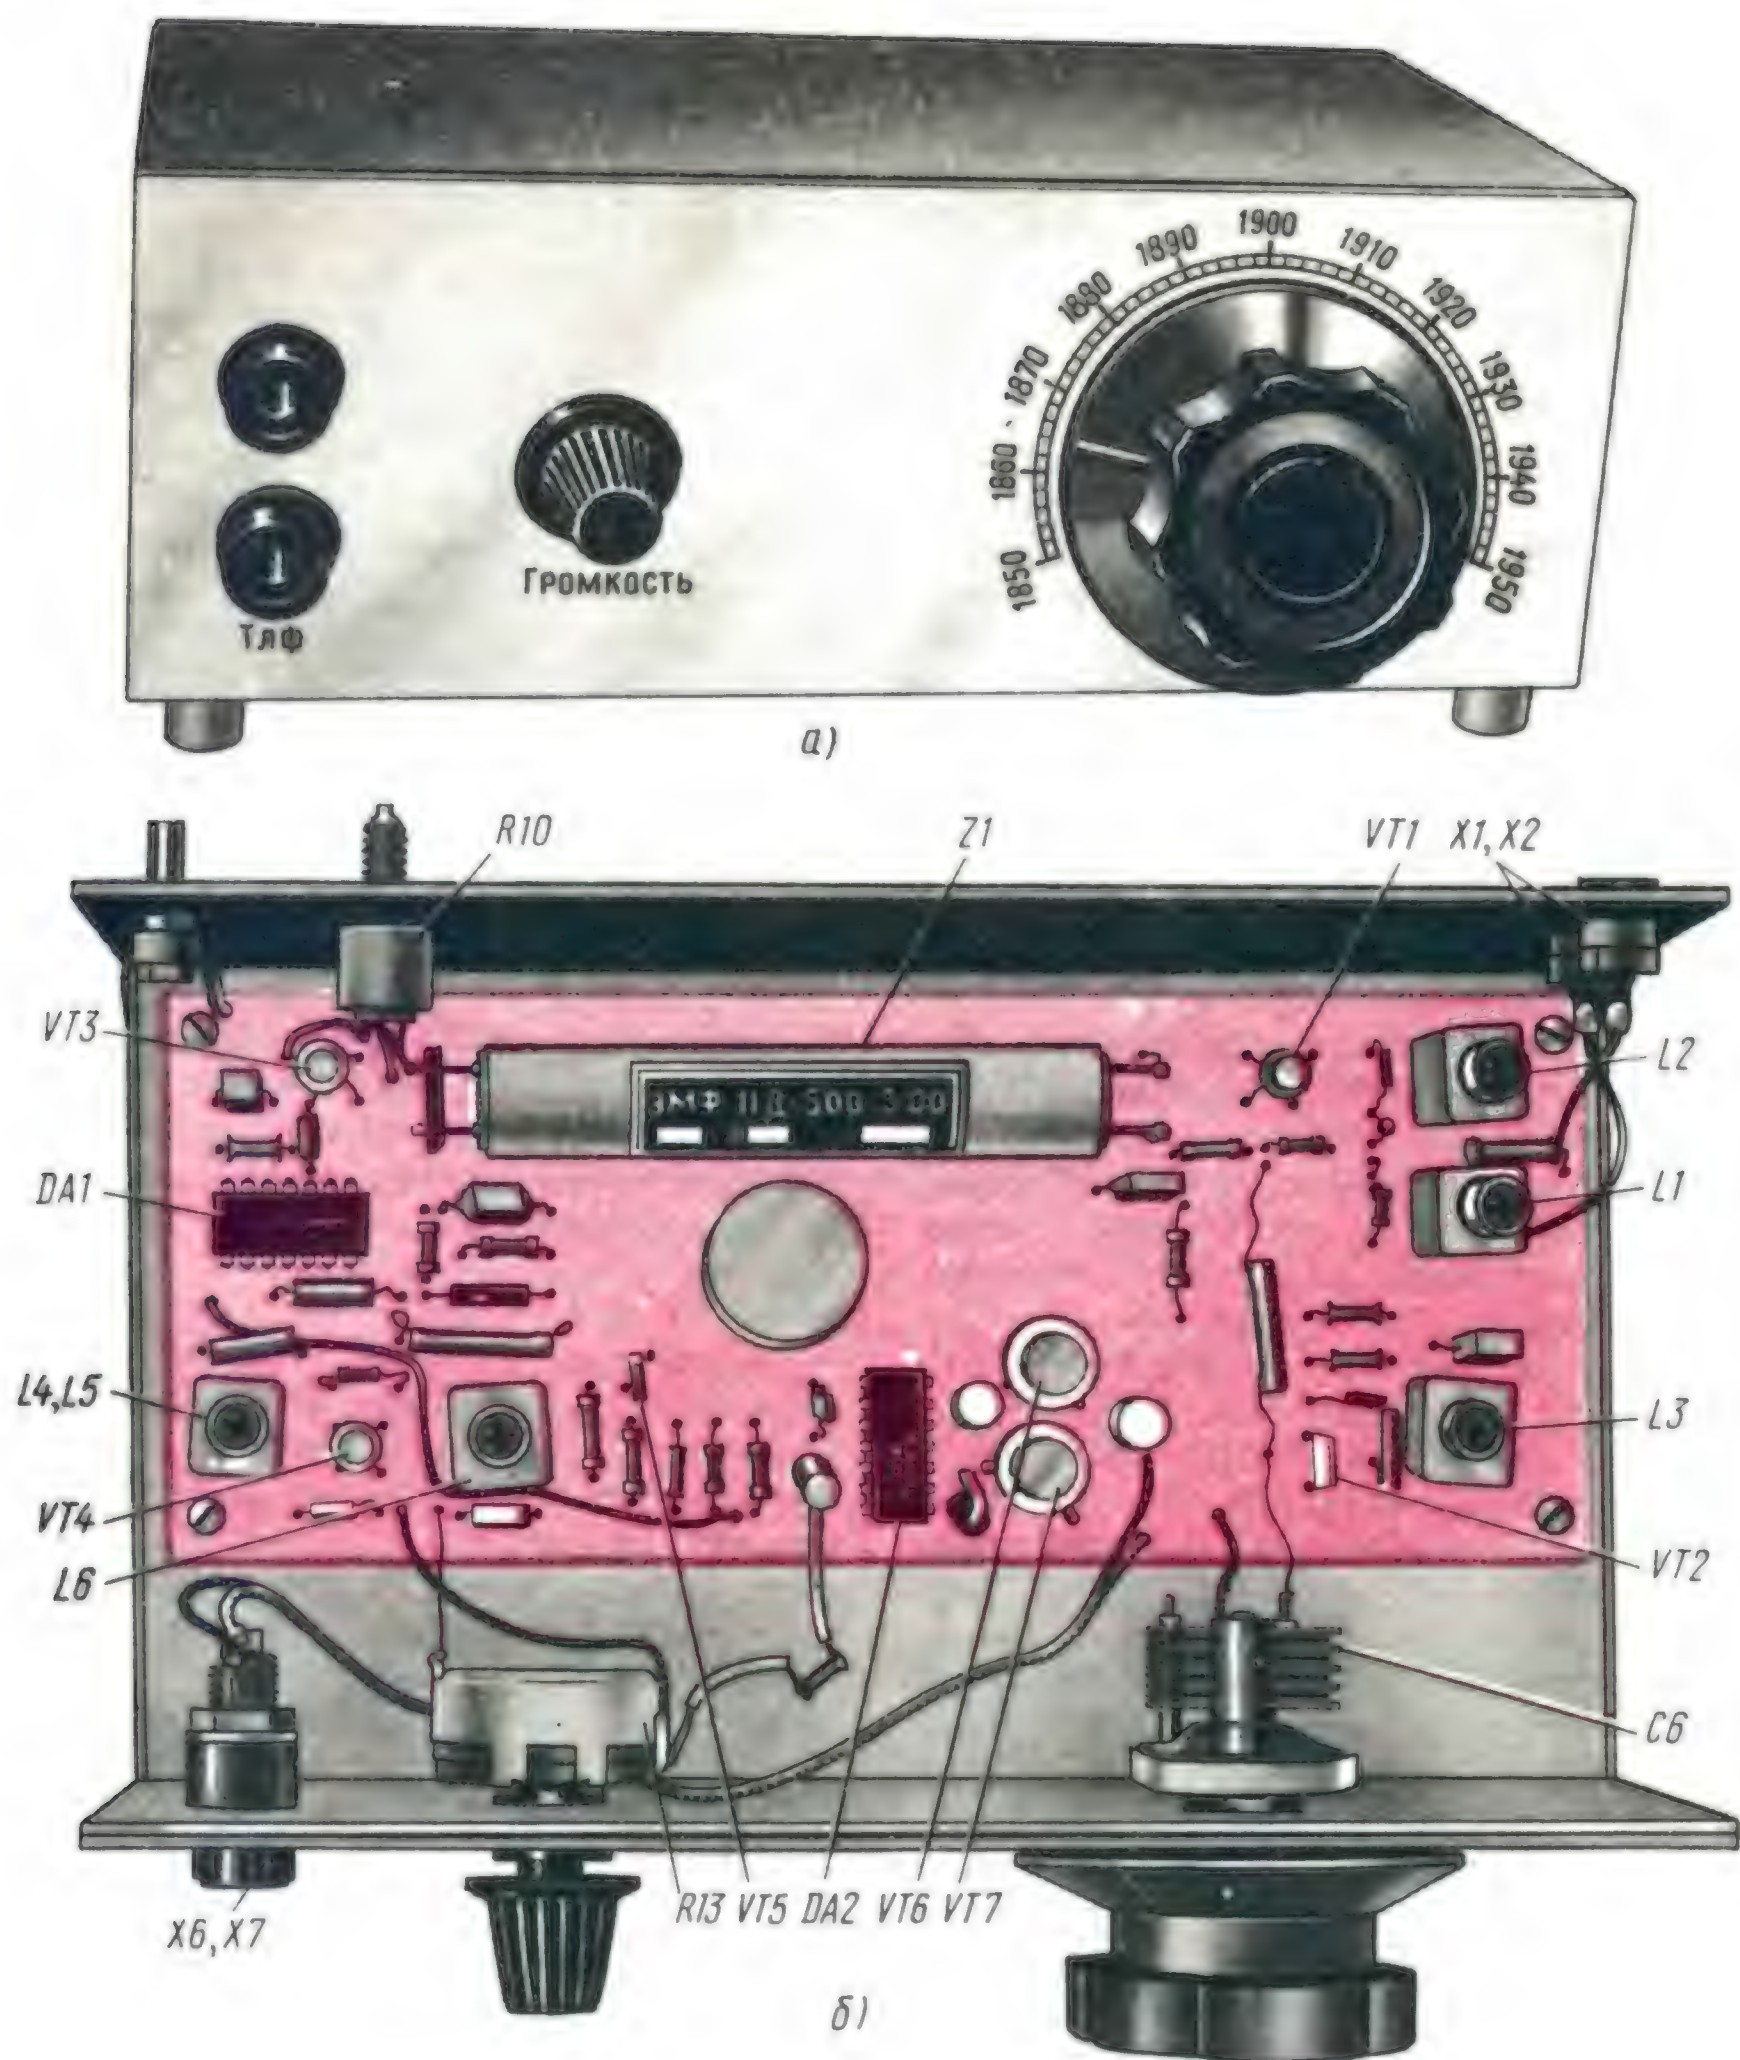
Внешний вид приемника (а) и размещение его платы и деталей в корпусе (б)
